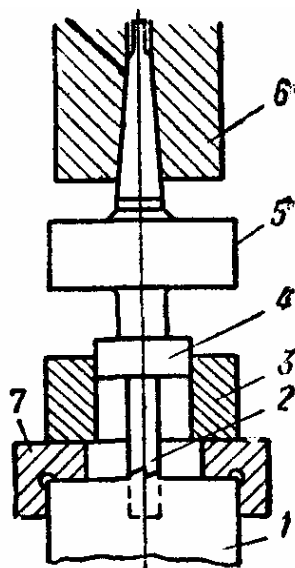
Схема копировального устройства для сверления шестигранных отверстий
